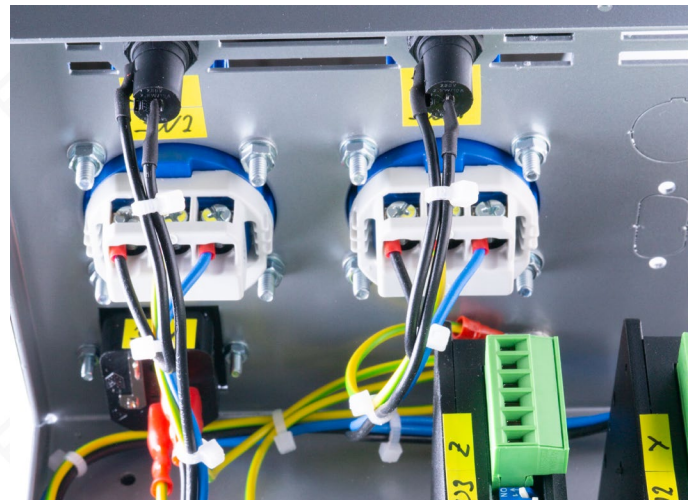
Die Steckdosen für Kühlung und Frässpindel mit Absicherung.
